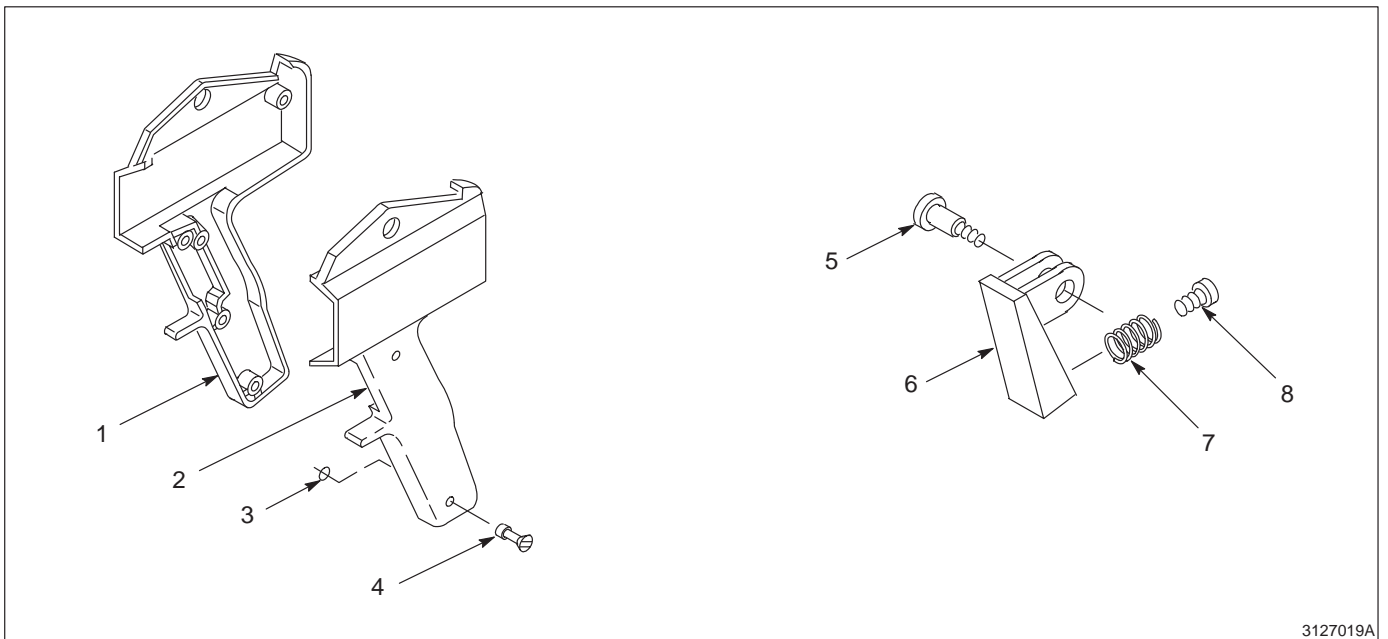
Kits de reposición de la empuñadura y del gatillo
